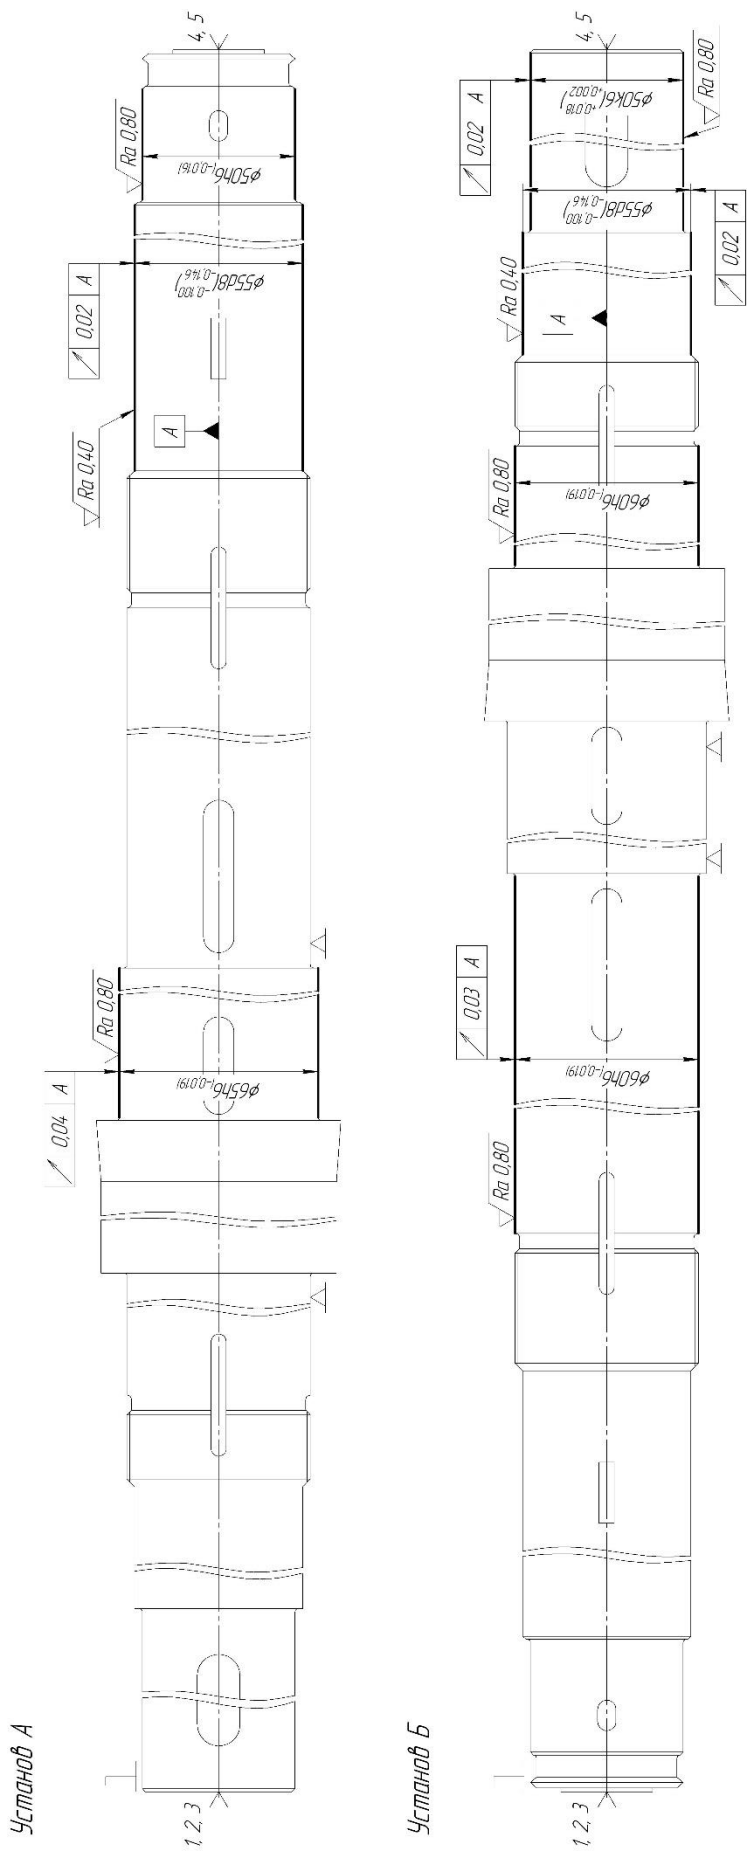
Схема базування заготовки на круглошліфувальній операції 045
